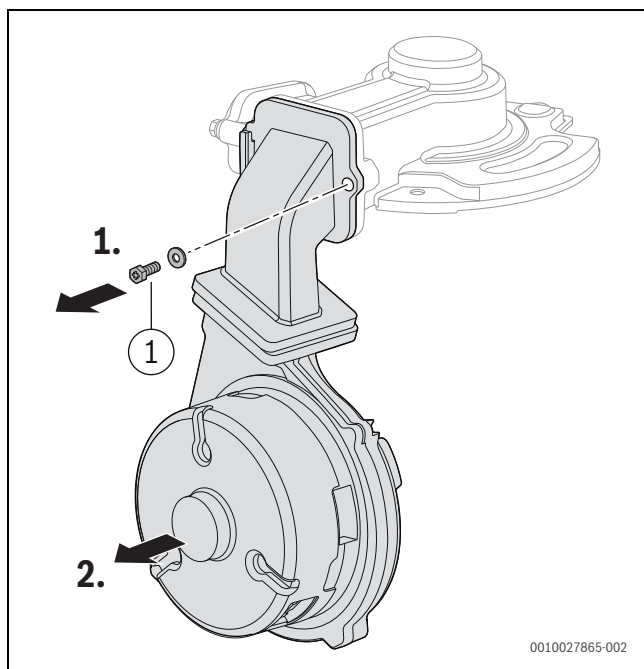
Odebrání krytu hořáku s ventilátorem a směšovacím zařízením
